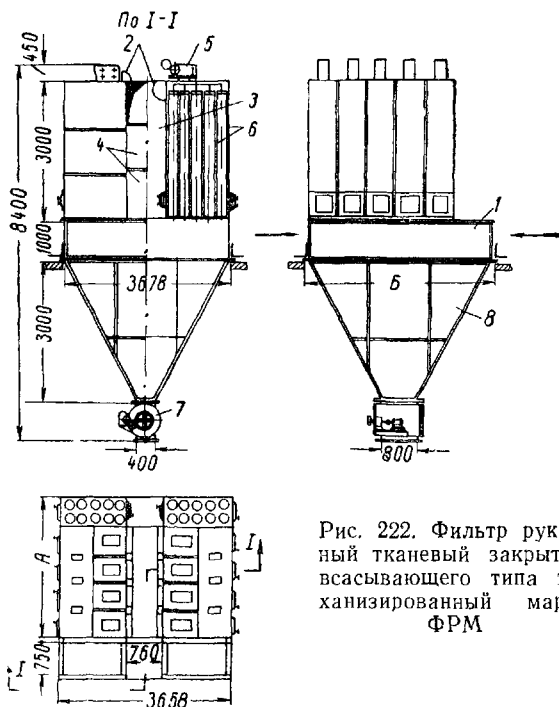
Фильтр рукавный тканевый закрытый всасывающего типа механизированный марки ФРМ
